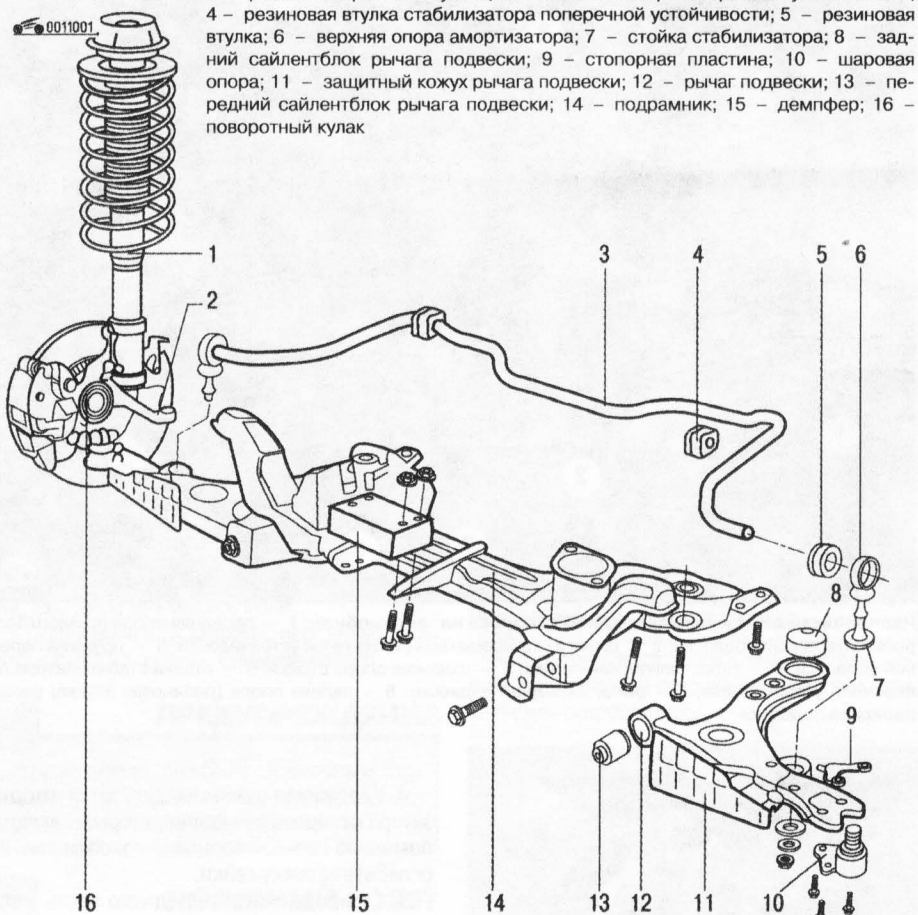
Передняя подвеска: 1 – телескопическая амортизаторная стойка; 2 – рычаг поворотного кулака; 3 – стабилизатор поперечной устойчивости; 4 – резиновая втулка стабилизатора поперечной устойчивости; 5 – резиновая втулка; 6 – верхняя опора амортизатора; 7 – стойка стабилизатора; 8 – задний сайлентблок рычага подвески; 9 – стопорная пластина; 10 – шаровая опора; 11 – защитный кожух рычага подвески; 12 – рычаг подвески; 13 – передний сайлентблок рычага подвески; 14 – подрамник; 15 – демпфер; 16 – поворотный кулак
